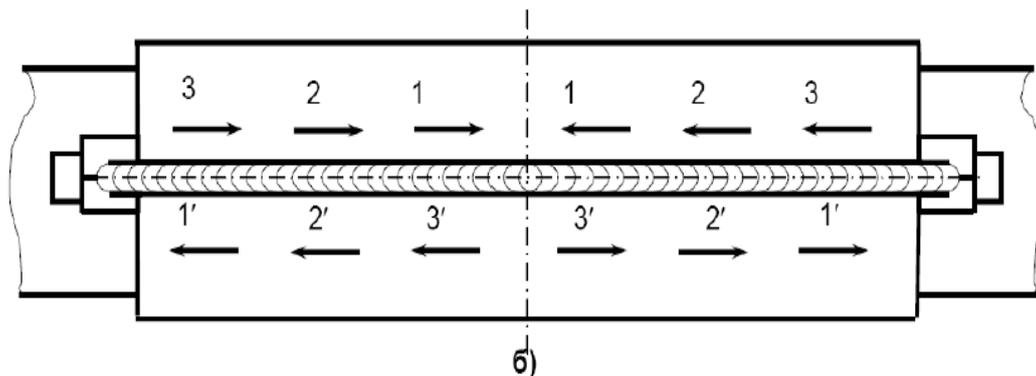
Проведение сварки одновременно четырьмя сварщиками при длине муфты $L > 600$ мм
